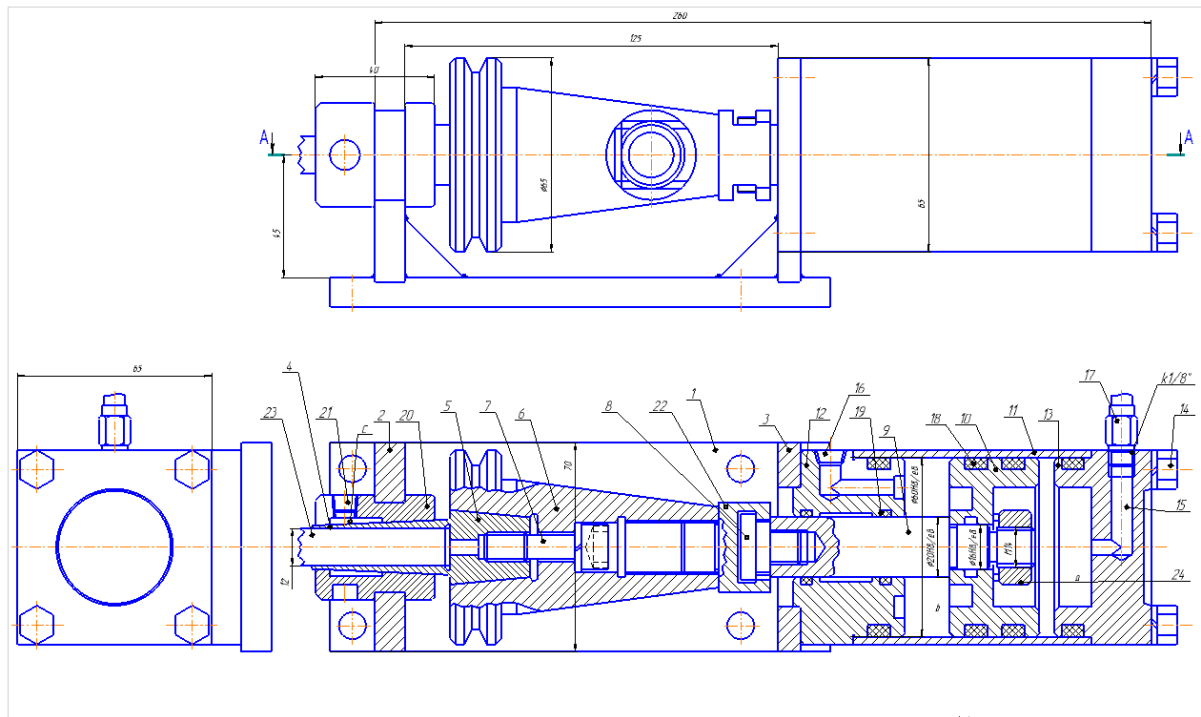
Пристрій для затиску – розтиску інструмента (деталі) в патроні.
